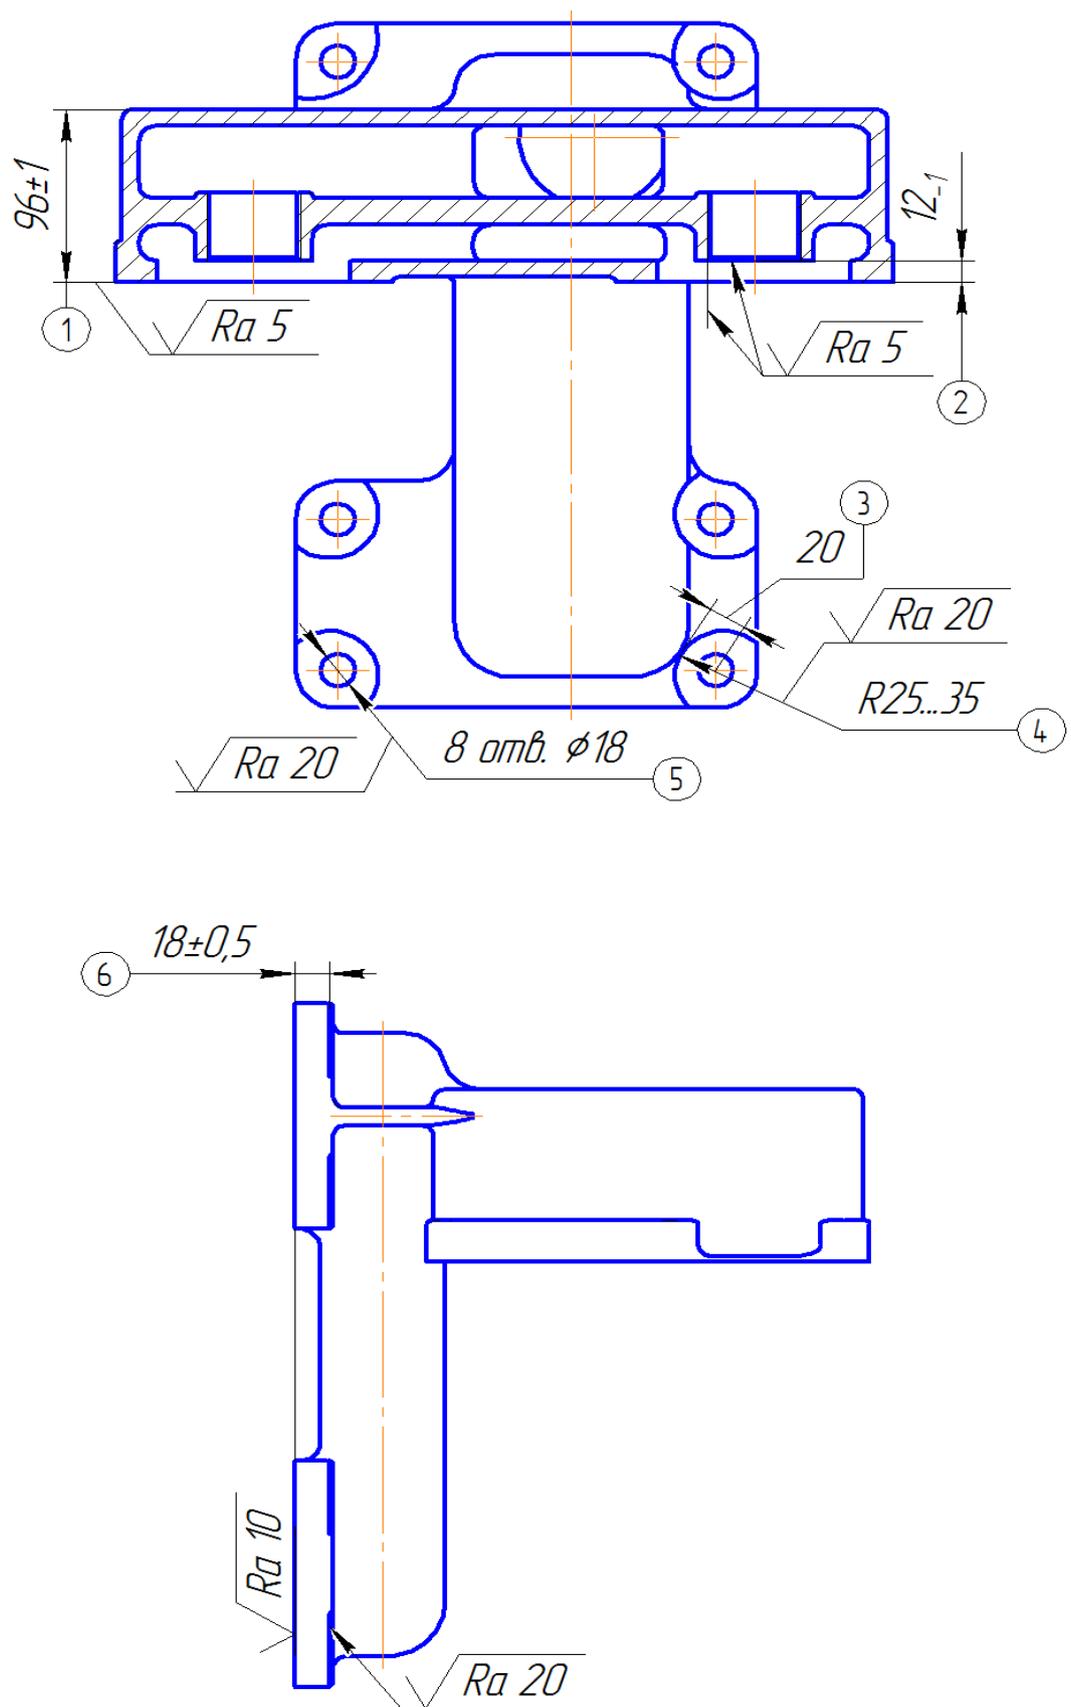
Эскиз детали «Корпус масляного фильтра»
